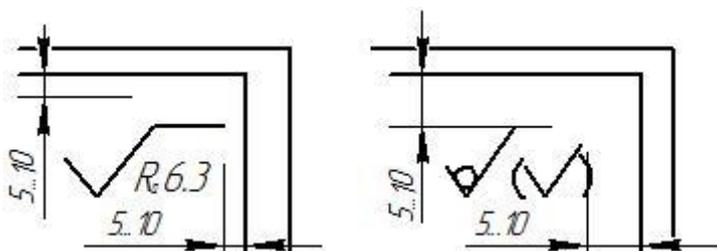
Правила обозначения шероховатости при разрывной детали
